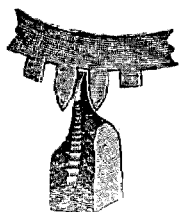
Установка заднего конца поводка при тонком фрезере.
